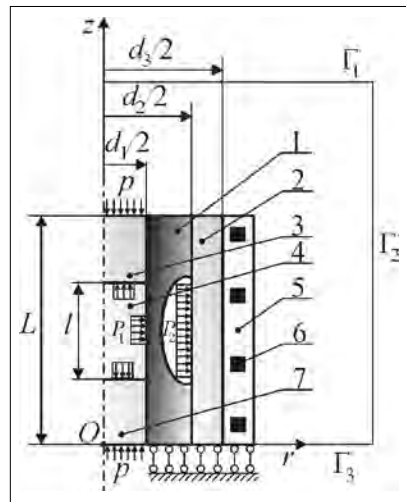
Розрахункова схема пристрою з індуктором для пресування порожнистих виробів з порошків: 1 – вкладиш; 2 – матриця; 3, 7 – пуансони; 4 – брикет з порошку; 5 – ізоляція індуктора; 6 – струмопровід індуктора
